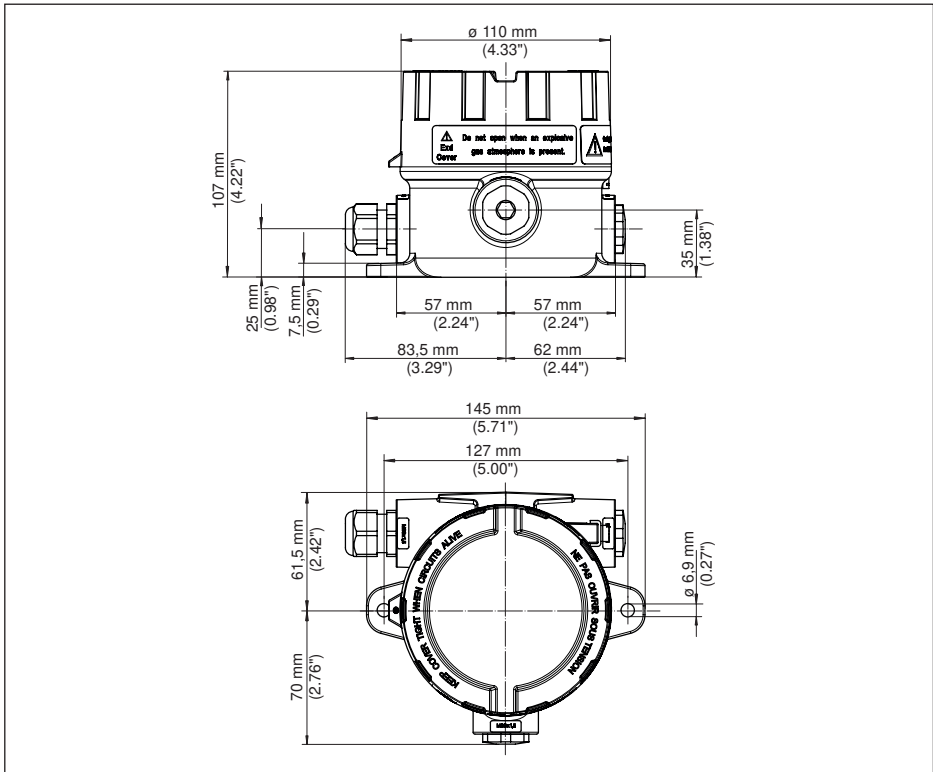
Размеры PLICSMOBILE B81 с алюминиевым корпусом
